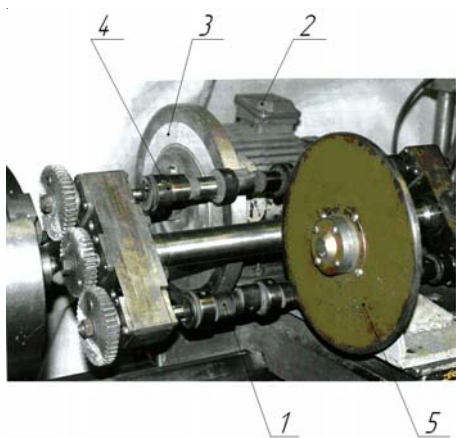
Приспособление к токарно-винторезному станку для шлифования кулачков распределительных валов:
